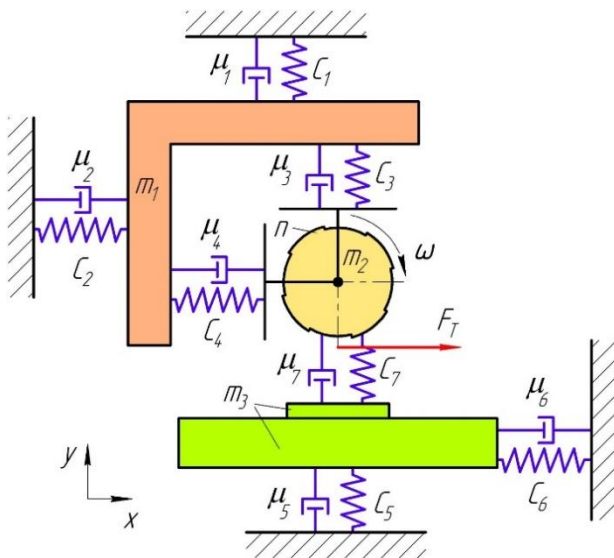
Розрахункова схема плоскошліфувального верстата
